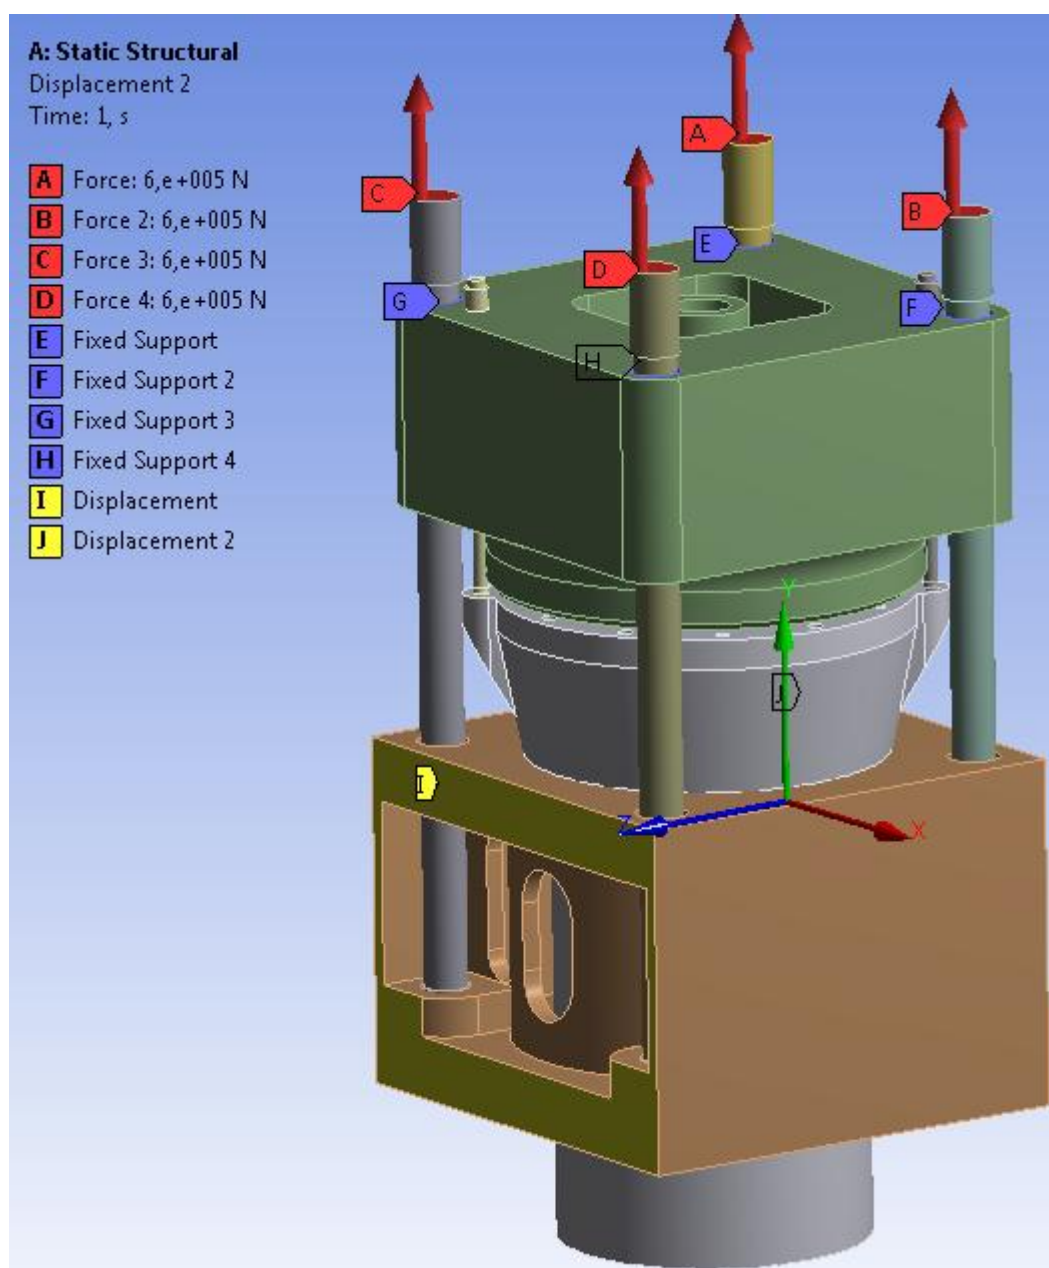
Твердотельная модель сборочного узла с условиями дополнительного нагружения и закрепления
